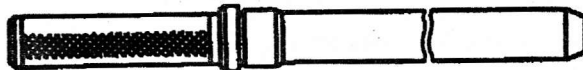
Оправка 7820-4797 для установки упорных шайб блока шестерен
